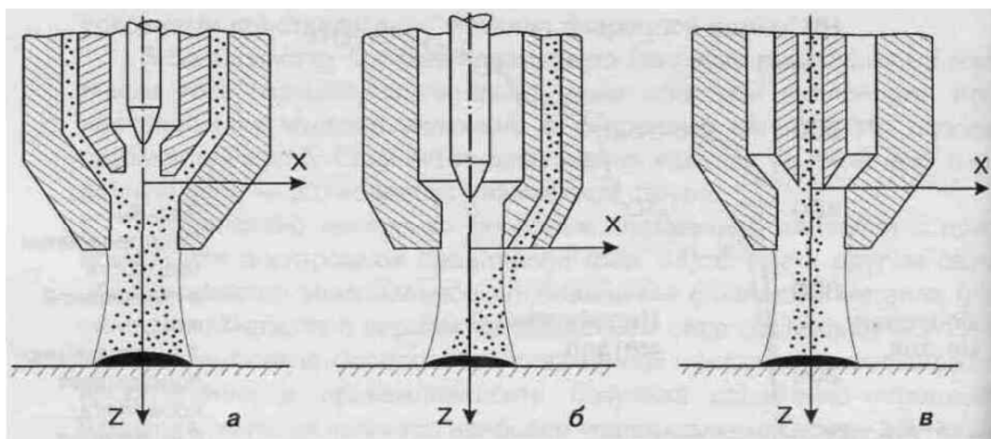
Схеми підведення порошку в дугу при плазмово-порошковій наплавці: а – розподілений через кільцеву щілину між соплами; б – локальний бічний через канал у торці сопла; в – аксіальний через порожнистий електрод
